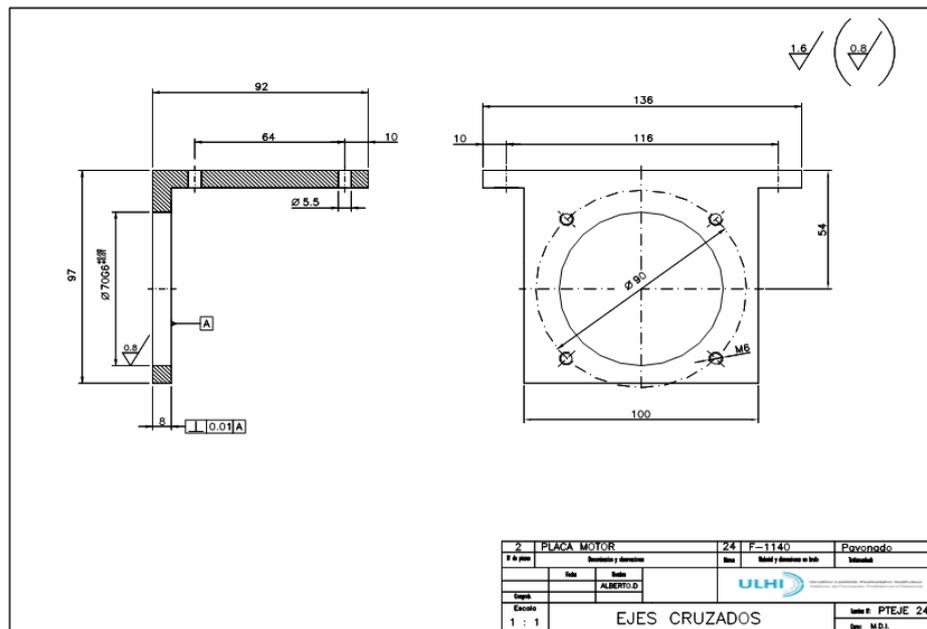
Ejemplo de plano de fabricación Fuente: Ikastaroak, (2020).
